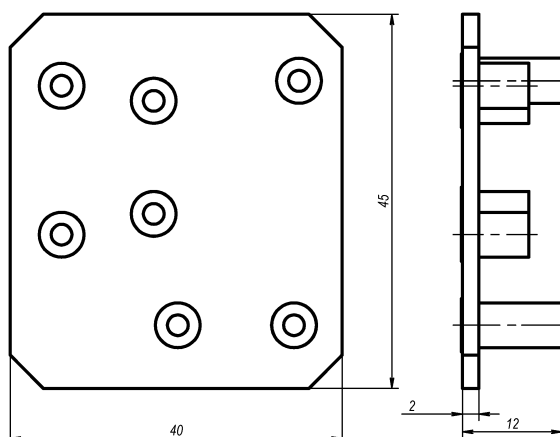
Шаблон для установки пружины EBKM.00D800.T2.01.000-01
